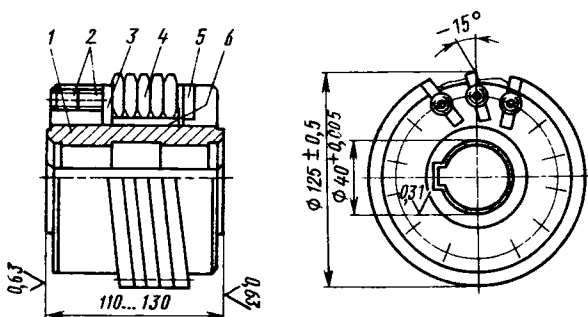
Сборочная червячная фреза с поворотными твердосплавными резцами
